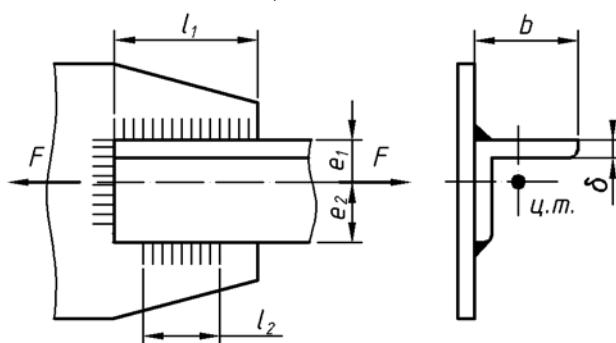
Сварное соединение полосы с косынкой
